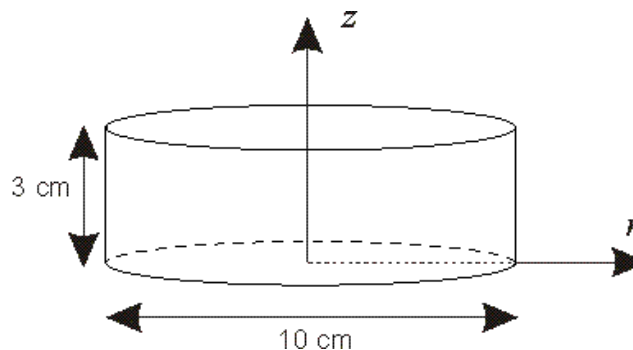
Dimensions de la pièce moulée en caoutchouc
